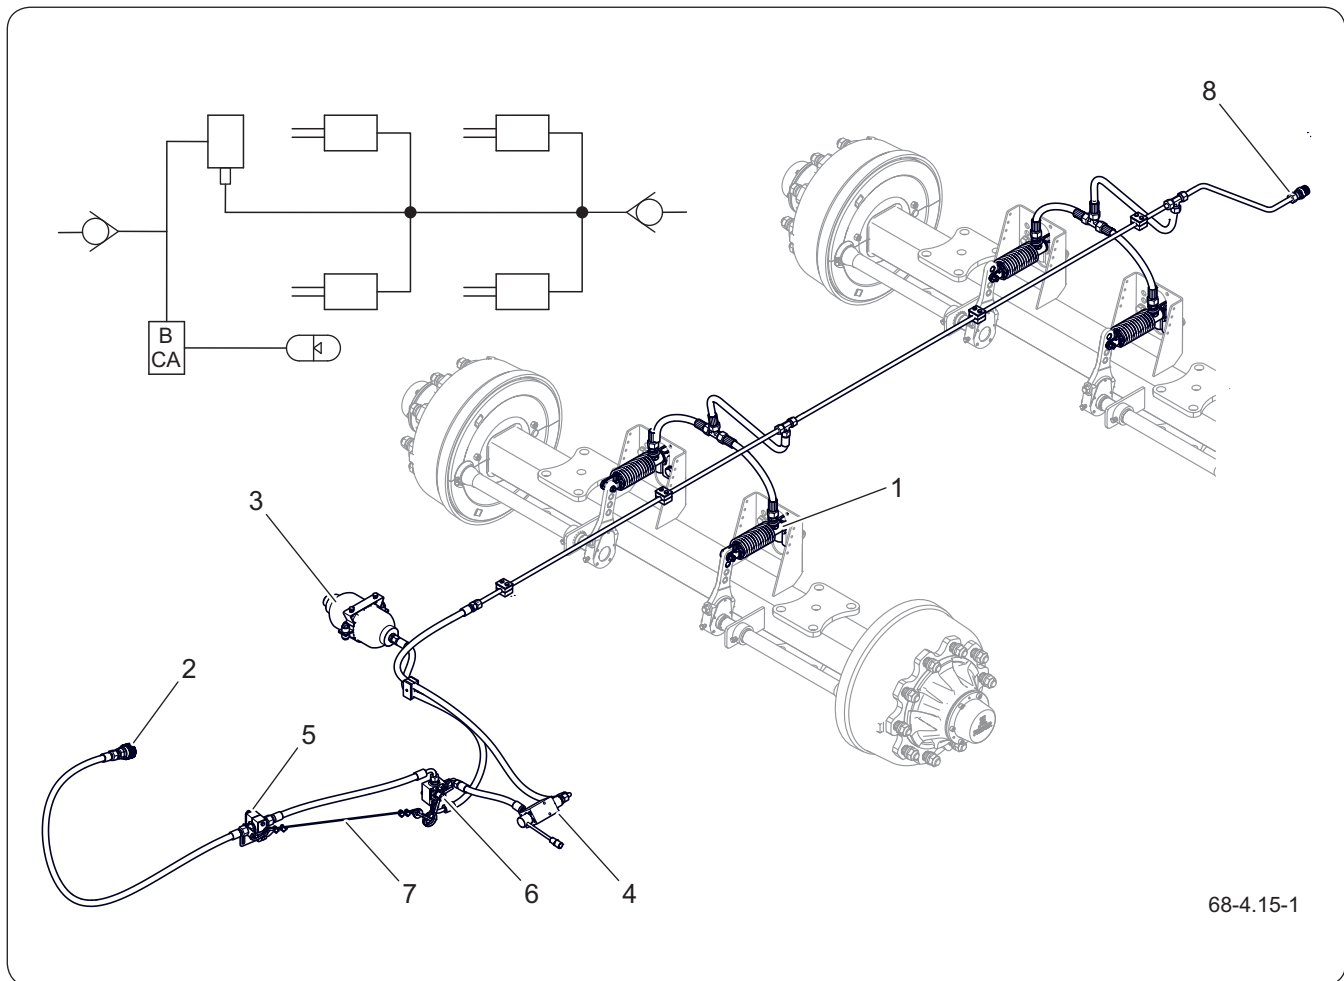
Schema und Aufbau der hydraulischen Bremsanlage
